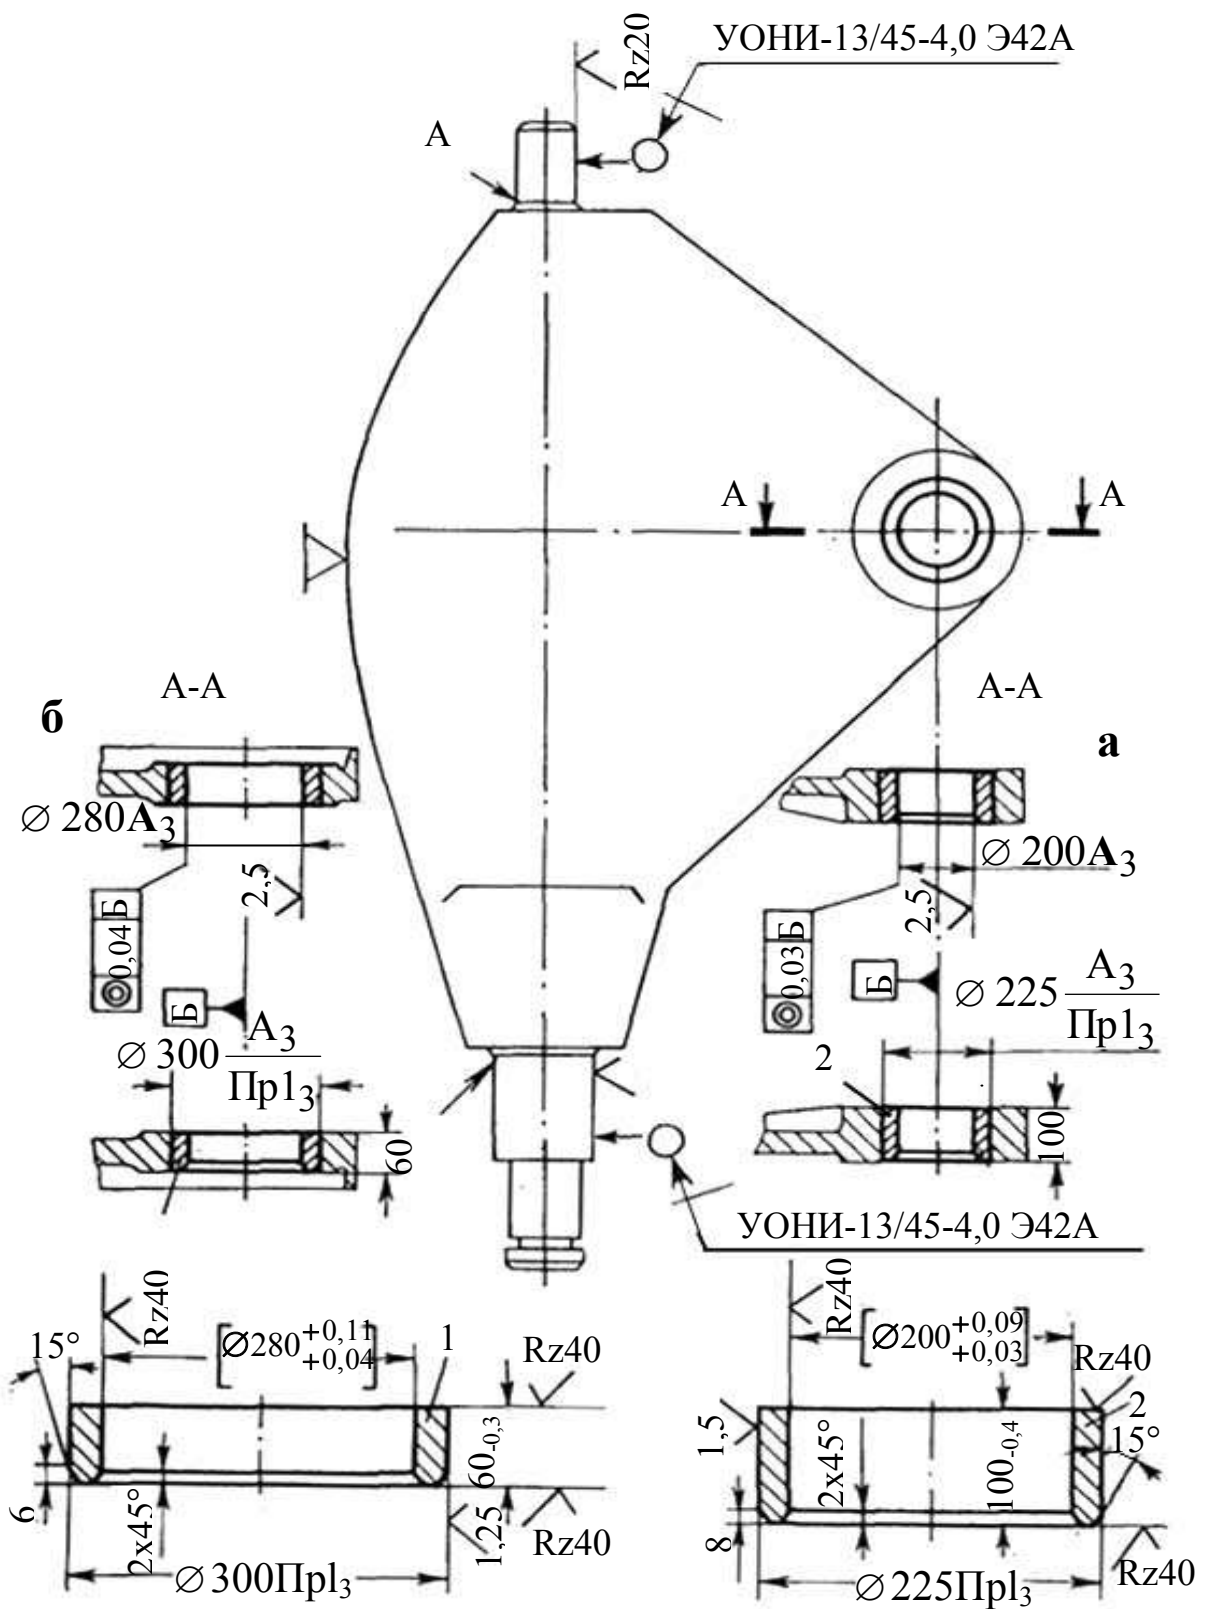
Ремонтный чертеж обойм направляющих блоков:
